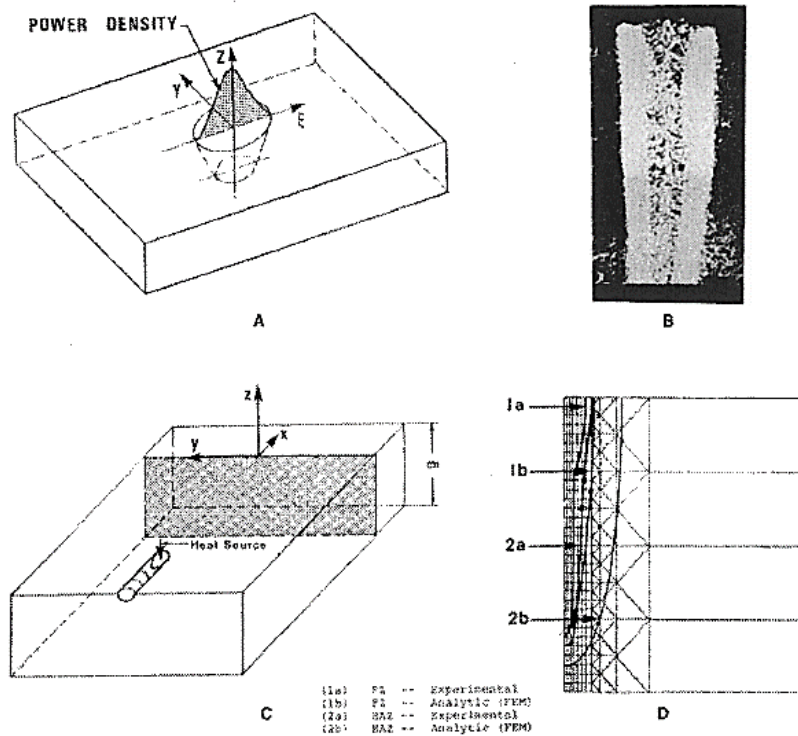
Fonte de calor para soldadura cônica usada na análise de penetrações de maior profundidade em soldadura por feixe de elétrons e laser. Fonte cônica (A), soldadura típica de soldadura por feixe de elétrons (B), corte transversal do modelo cinemático com um plano de referência (C), zona de fusão computacionada e medida e ainda zona termicamente afetada e suas fronteiras ( $V=70$  kV,  $I=40$  mA,  $v=4.23$  mm/s,  $g=12.7$  mm e  $T_0=21$  °C), [14].
